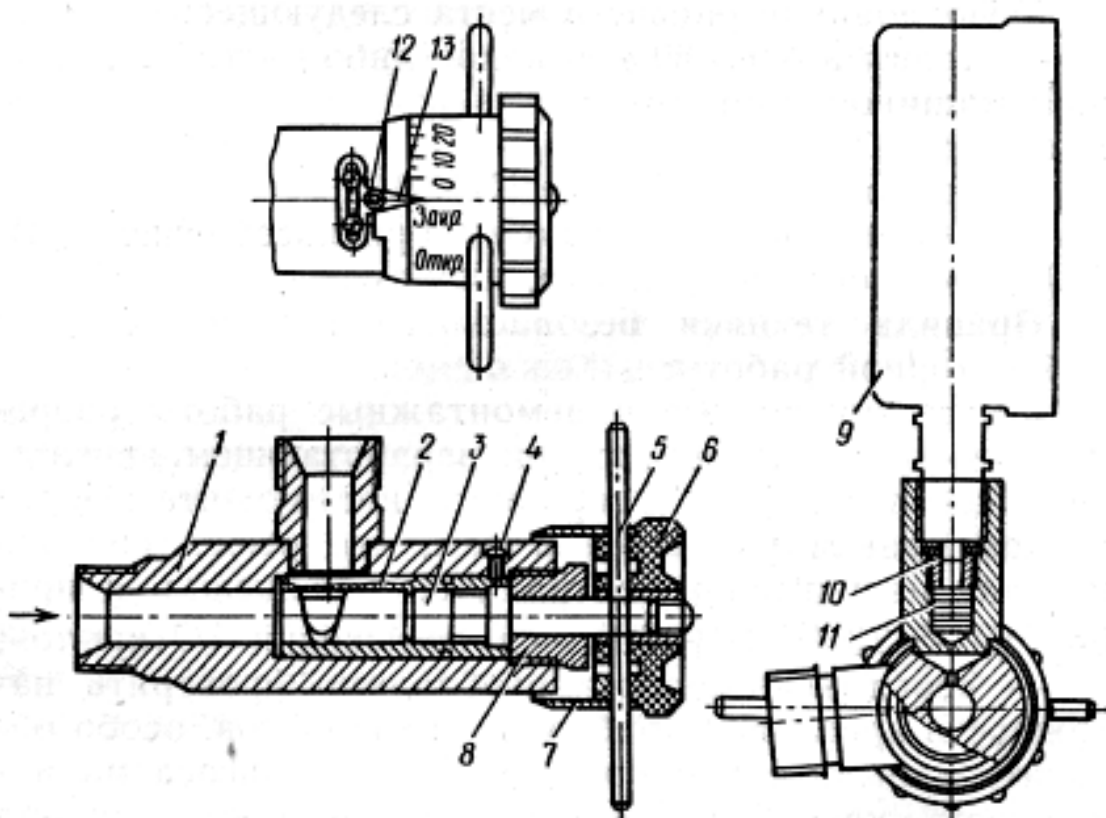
Прибор КИ-1097-1: 1 — корпус; 2 — дроссель; 3 — плунжер; 4 — установочный винт; 5 — стержень; 6 — рукоятка дросселя; 7 — лимб; 8 — упорная гайка; 9 — манометр; 10 — специальная гайка; 11 — шайба демпфера; 12 — ограничитель; 13 — стрелка-указатель.
